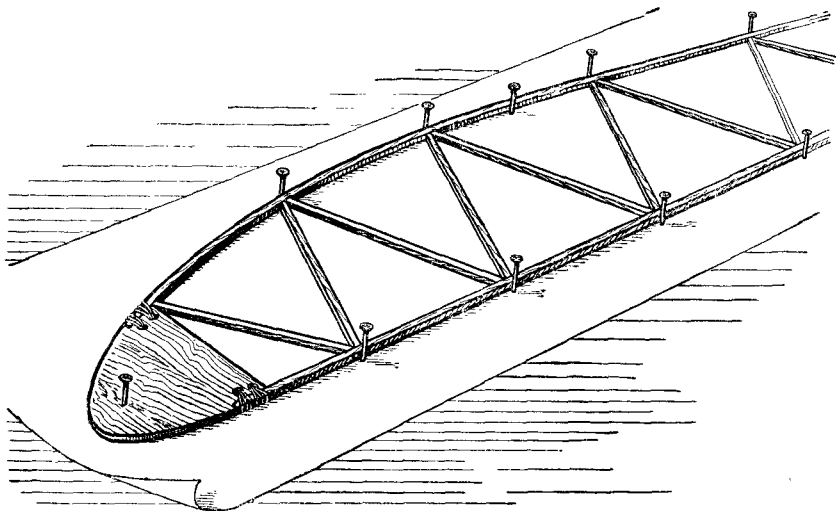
Сборка боковой фермы фюзеляжа на рабочем чертеже
